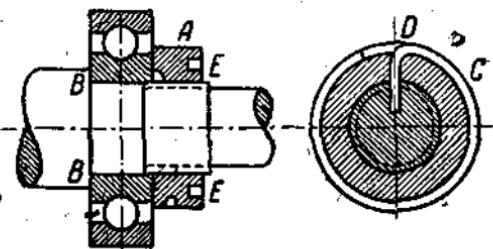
Крепление шарикоподшипника с помощью гайки.
